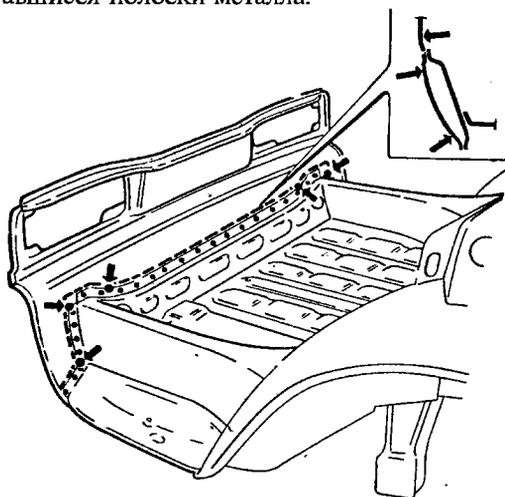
Замена панели задка. Пунктиром обозначены линии рубки, точками - швы контактной сварки. На основном виде стрелками показаны места газовой сварки, стрелками на фрагменте - места рубки
